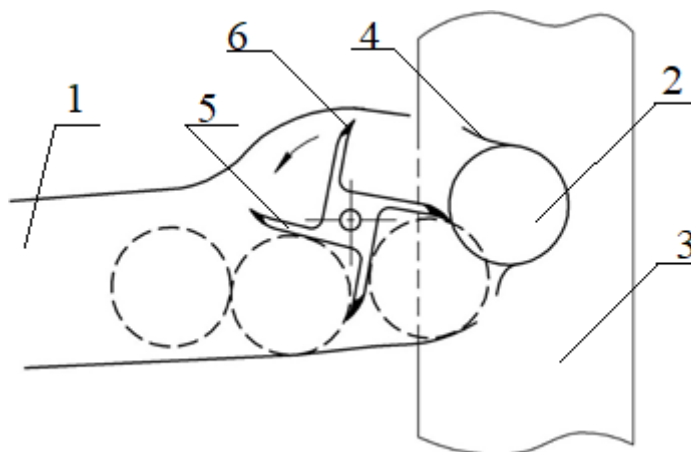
Схема загрузочного устройства банок на ленточный конвейер
